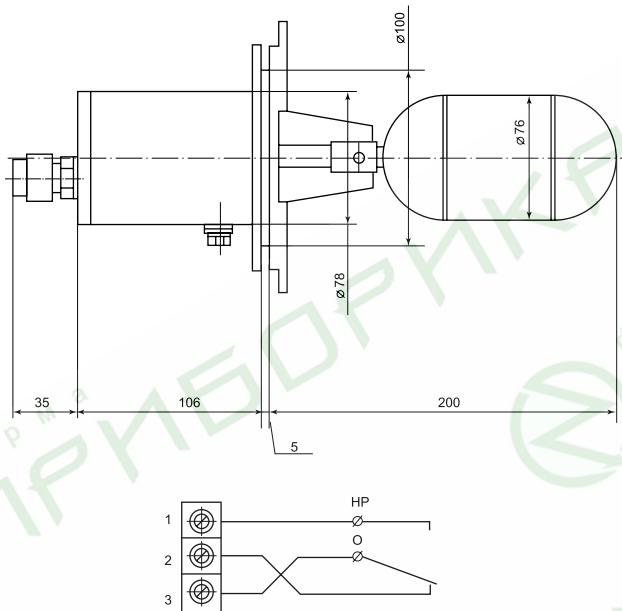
Габаритные и присоединительные размеры РОС 400-7
